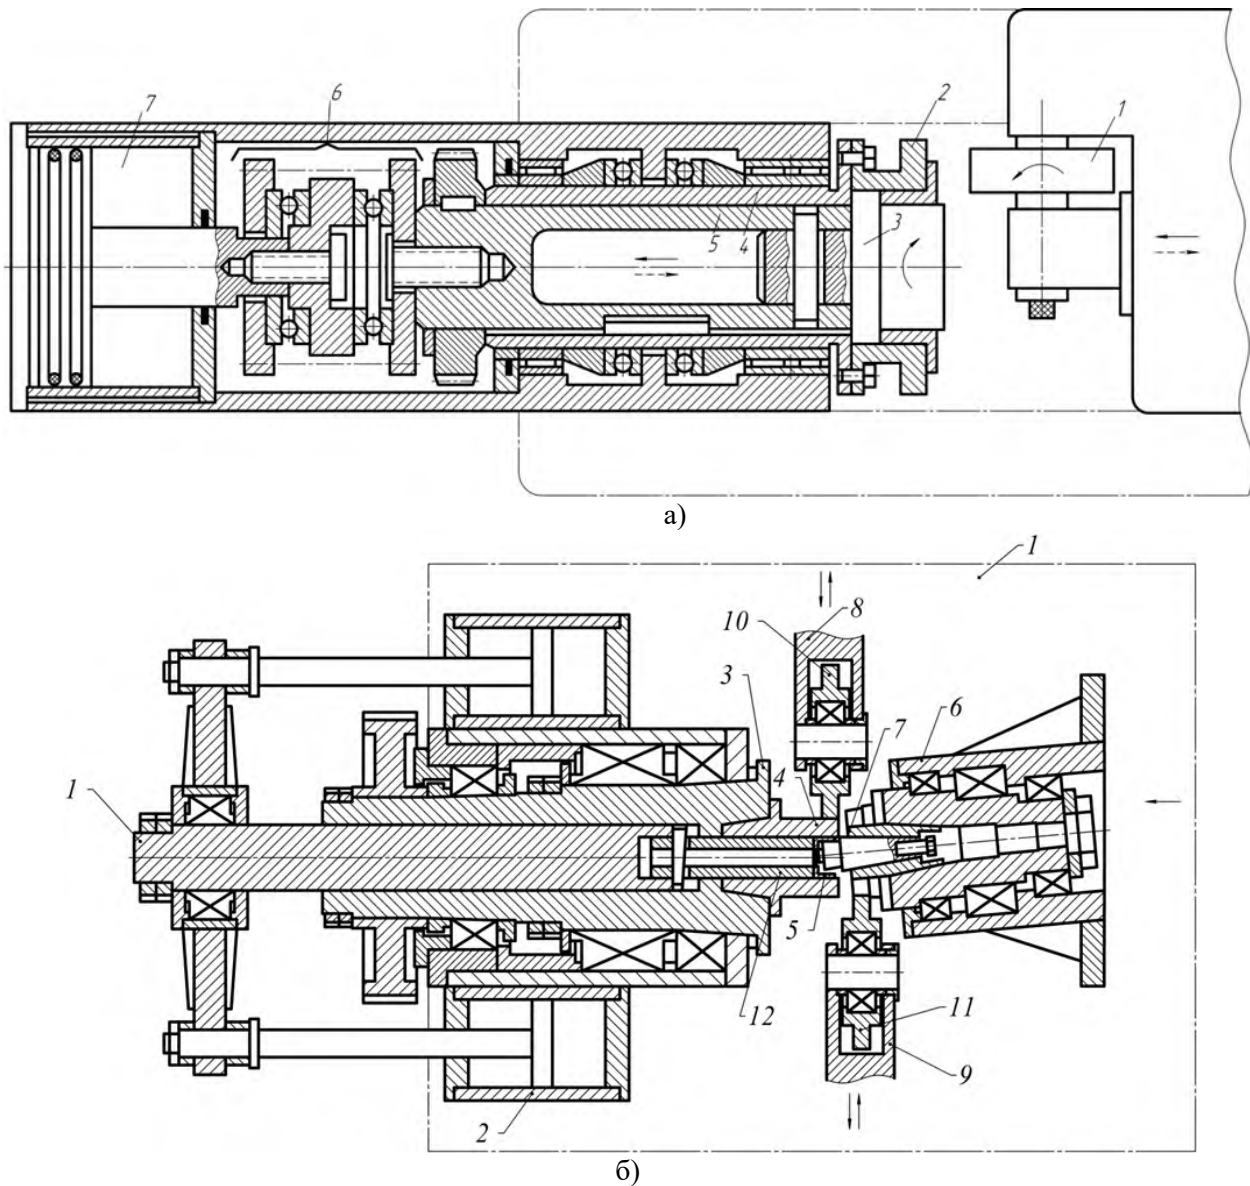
Обкочувальні інструментальні блоки для виготовлення складно профільних заготовок:
